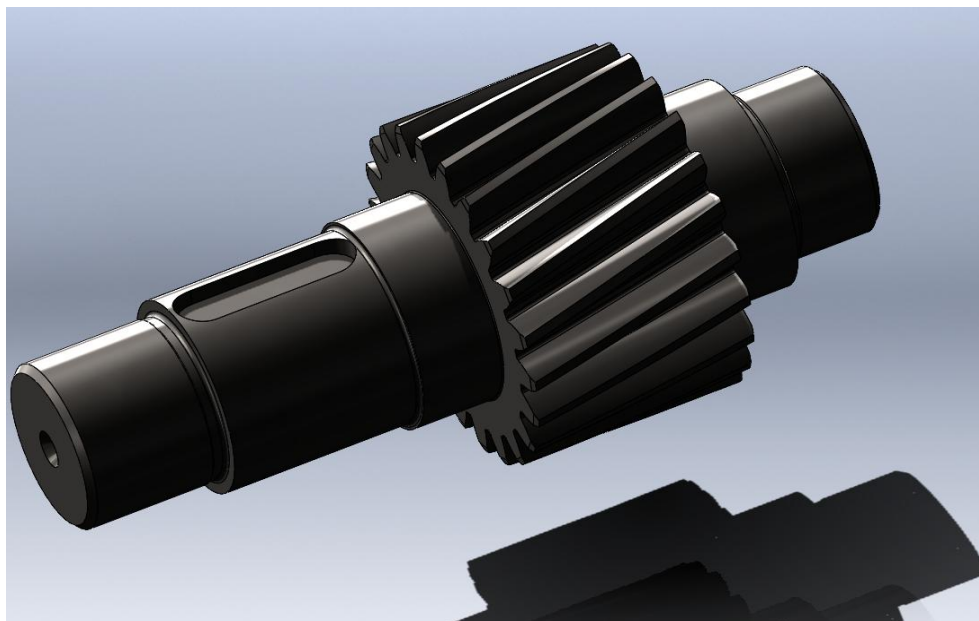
Загальний вигляд валу-шестерні другої ступені конічно-циліндричного редуктора
